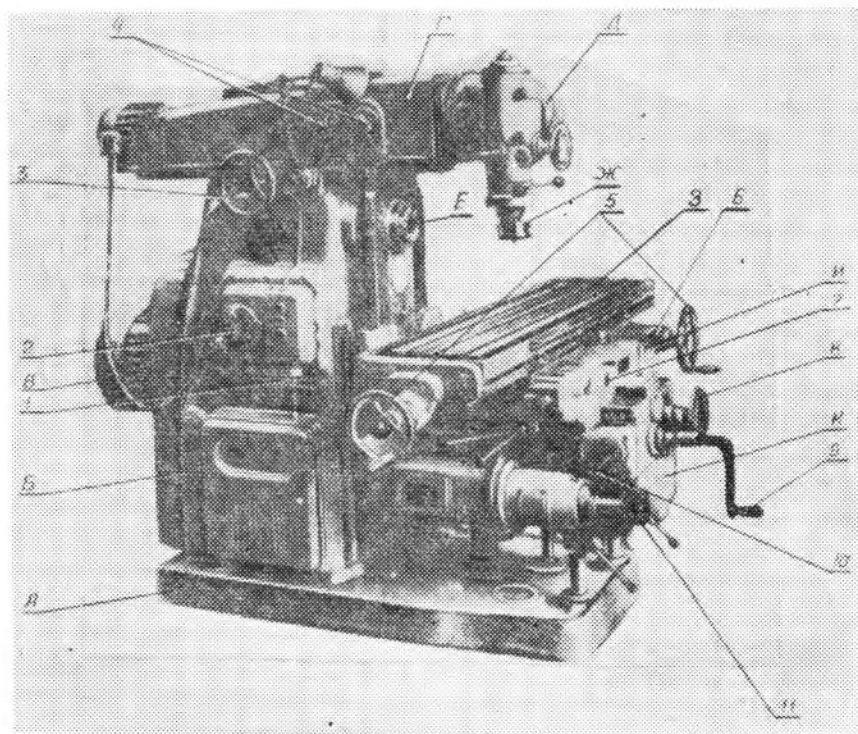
Широкоуниверсальный фрезерный станок 61183Ш1:
